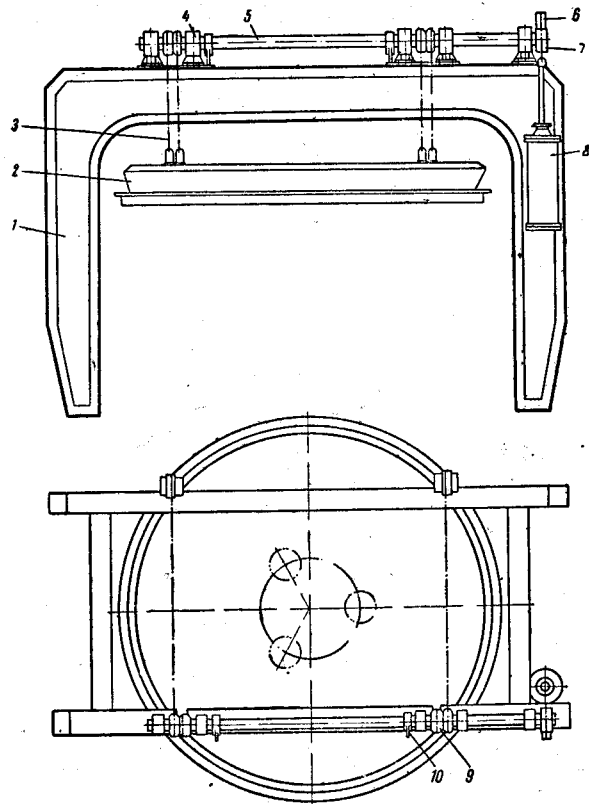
Механизм подъема свода печей серии ДСВ. 1 — портал; 2 — сводовое кольцо; 3 — цепная подвеска; 4 — подшипник; 5 — вал; 6 — ведущий сектор; 7 — тяговая цепь; 8 — гидрочилиндр; 9 — цепной блок; 10 — упор.
